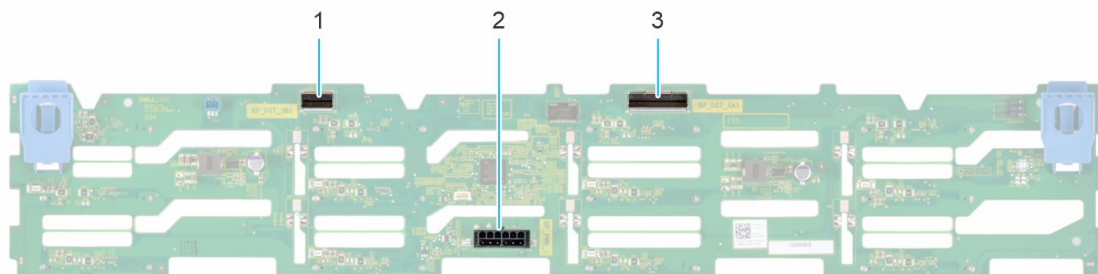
Fond de panier de 8 disques de 3,5 pouces
